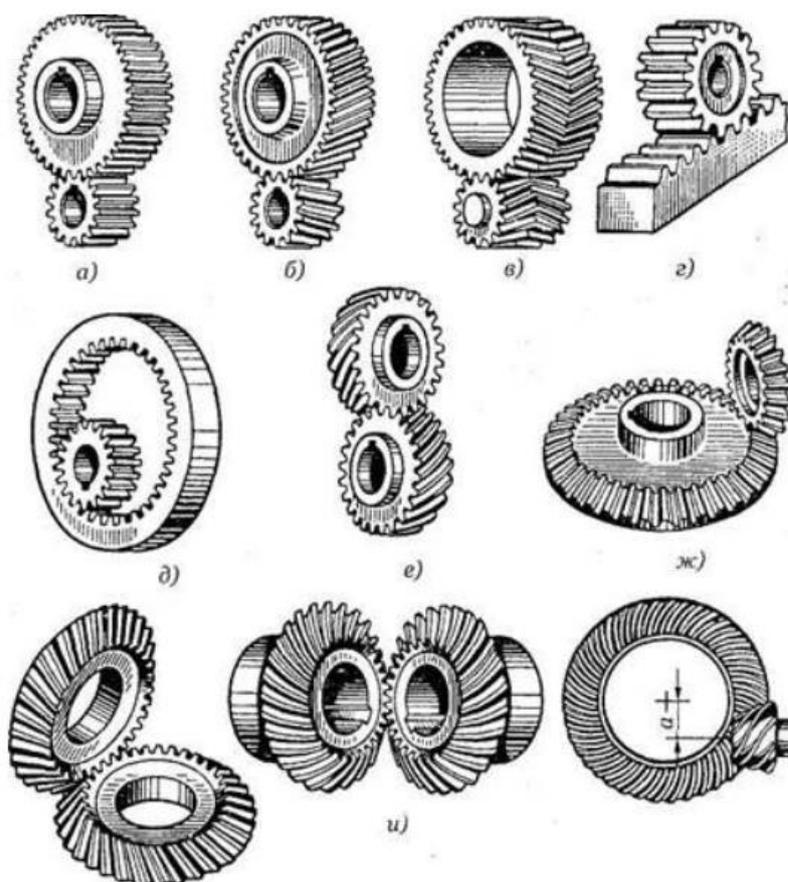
Виды зубчатых передач: а, б, в - цилиндрические зубчатые передачи с внешним зацеплением (прямозубая, косозубая и шевронная); г - реечная передача; д - цилиндрическая передача с внутренним зацеплением; е - зубчатая винтовая передача; ж, з, и - конические зубчатые передачи; к - гипоидная передача.
